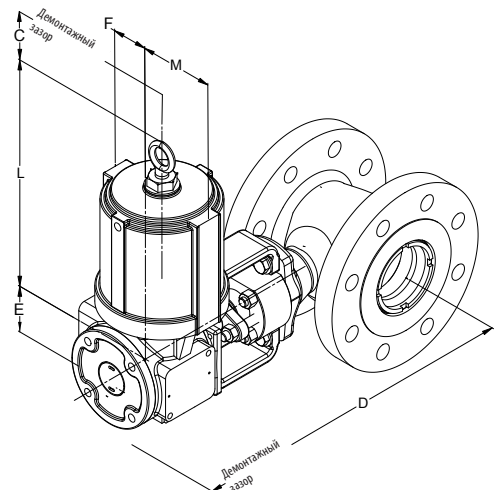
Привод с пружинным цилиндром MaxFlo 4
